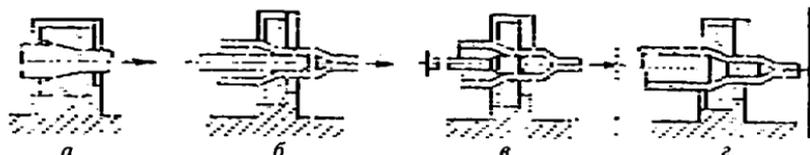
Схемы волочения: а — прутка; б — трубы; в — на неподвижной оправке; г — без неподвижной оправки
